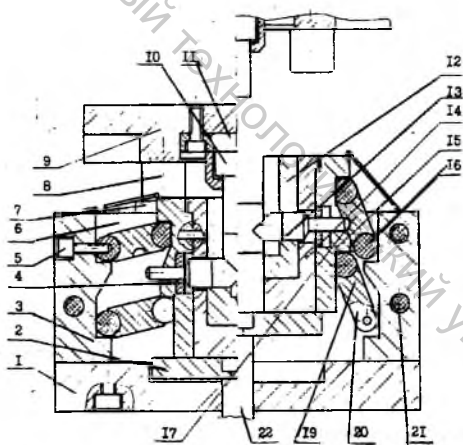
Пакет рычажный с вертикальным разъемом матриц.
